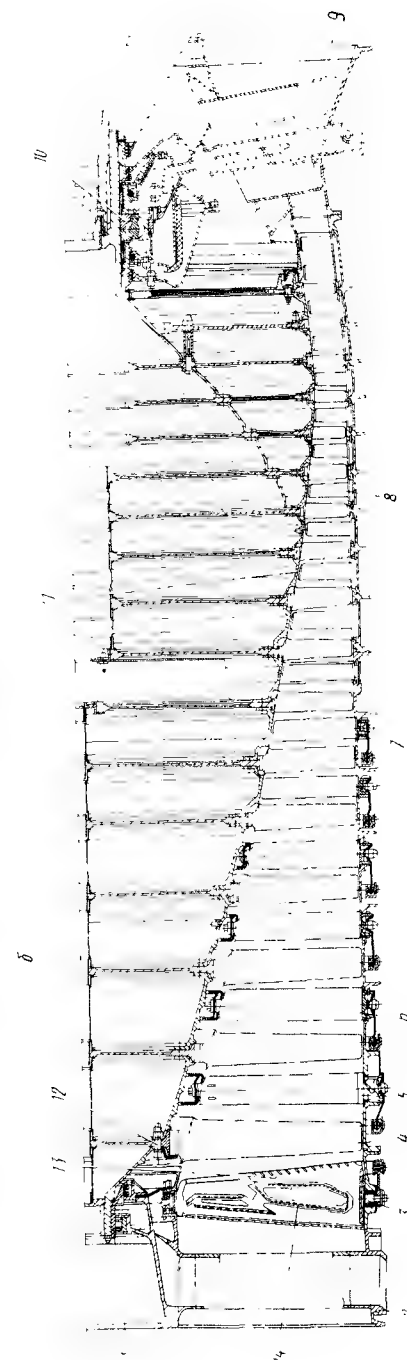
Однокаскадный компрессор с поворотными лопатками направляющих аппаратов:
